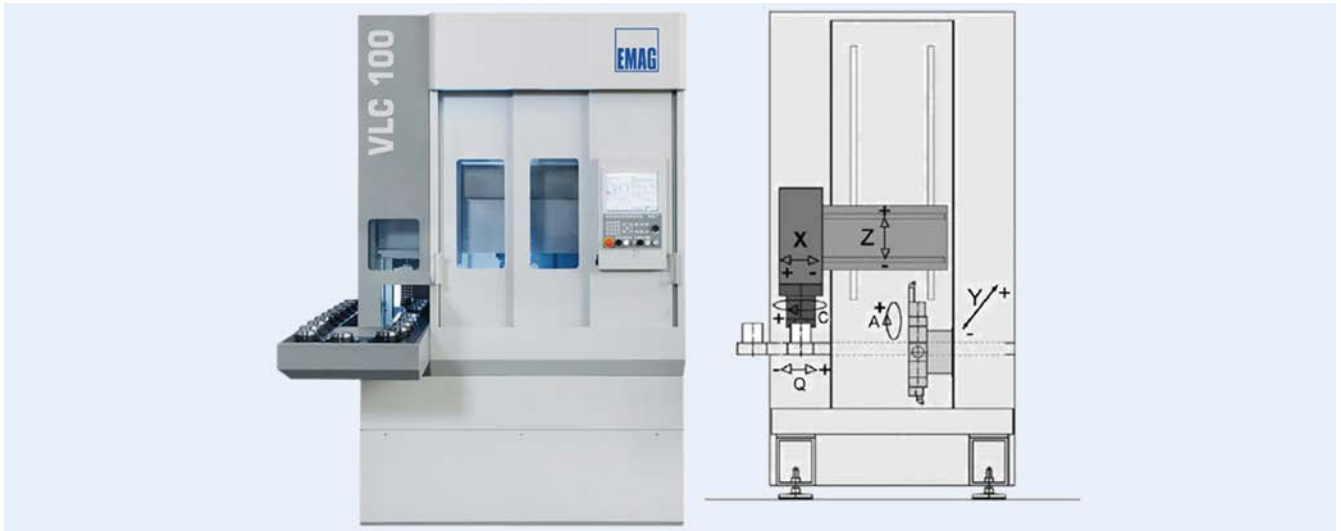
Versuchsmaschine Emag (links) mit ihren Maschinenachsen (rechts). Bild: Emag
